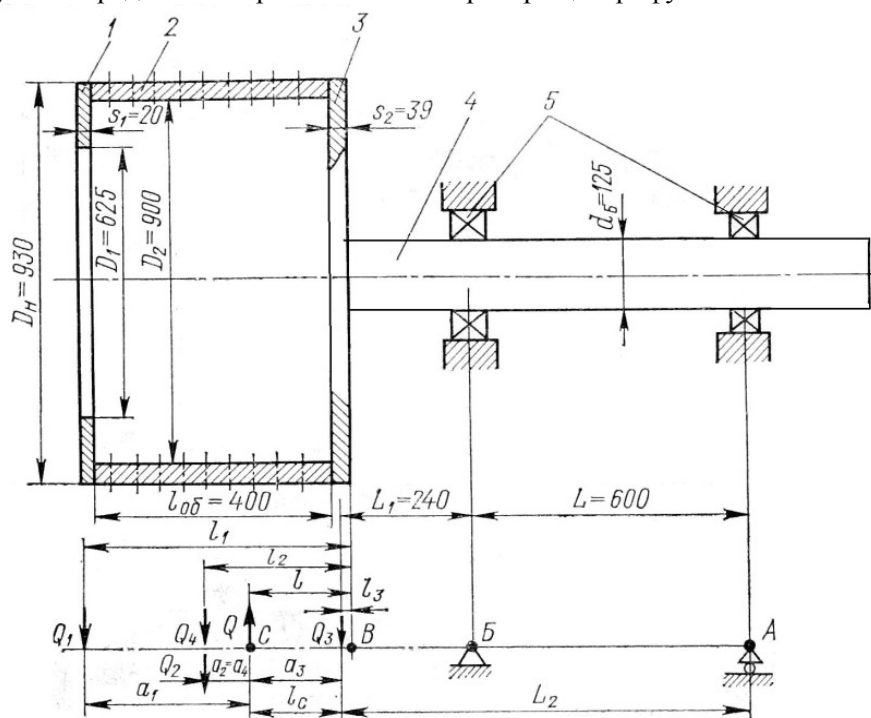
Расчётная схема ротора центрифуги с консольным валом: 1 – плоский диск; 2 – обечайка; 3 – днище; 4 – вал; 5 – подшипник
